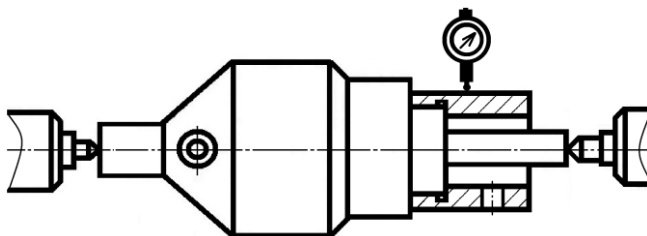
Схема измерения биения заготовки, установленной на оправке
